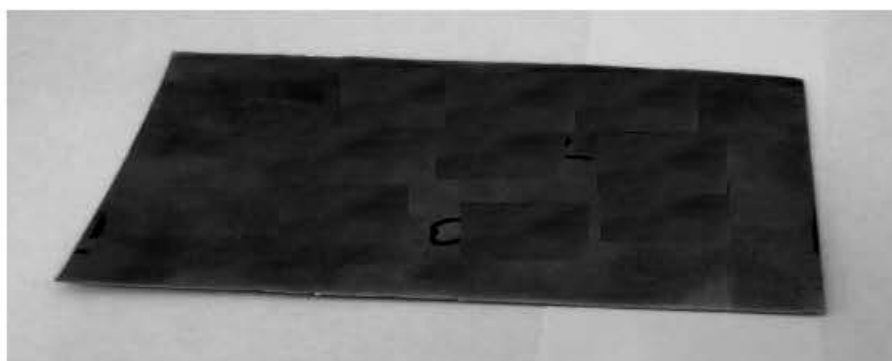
Зразок для обробки на дробеметній установці
